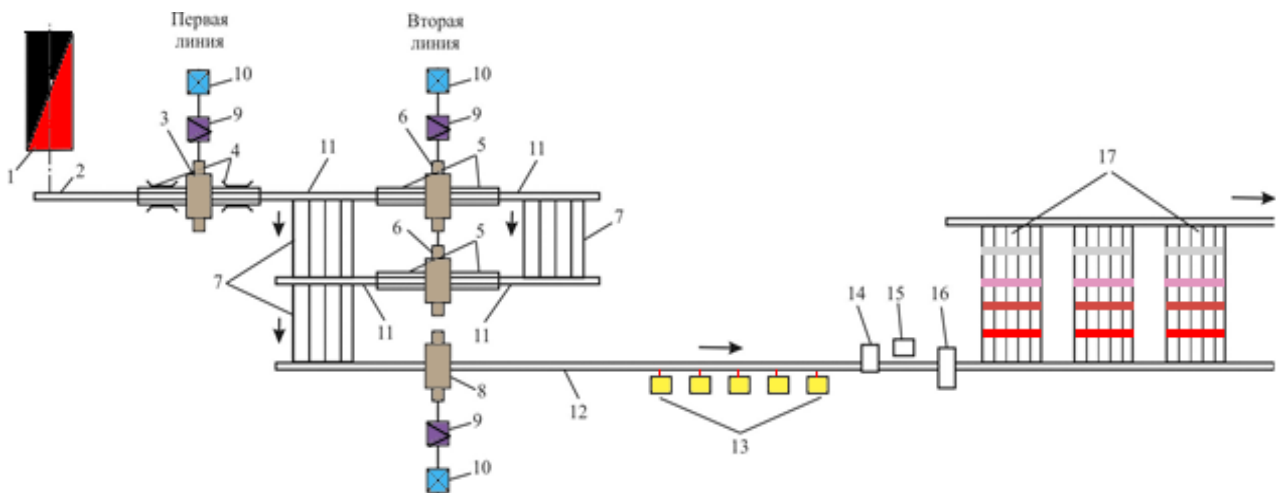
Схема рельсобалочного стана 900/800 ПАО «МК «Азовсталь»» [4]:
